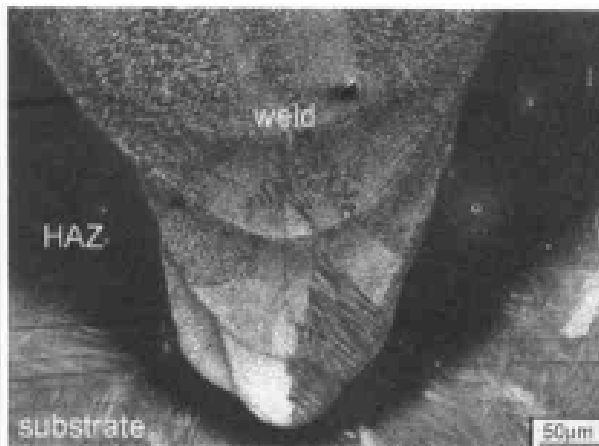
激光焊接, 42CrMo 合金/42CrMo 合金, CO<sub>2</sub> 激光, 焊缝底部, 功率 2800W, 焊接速度 1.75m/min
